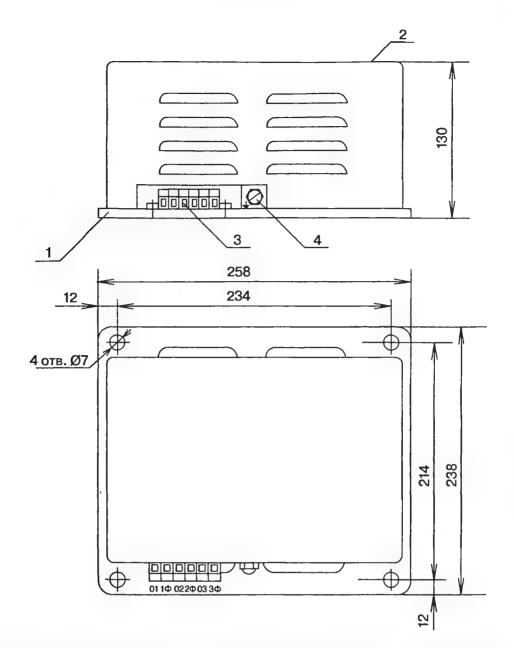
Внешний вид блока БЗПЗ-25 и БЗПЗ-100, где: 1— основание; 2— кожух; 3— клеменной соедининтель; 4— винт заземления
